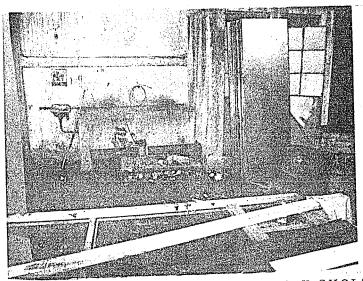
PLANTA DESORDENADA Y SUCIA
